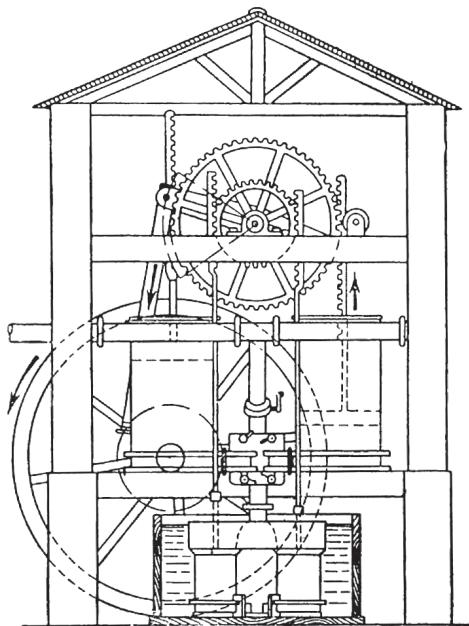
5 Двигатель Фалька, суммирующий работу двух цилиндров.
